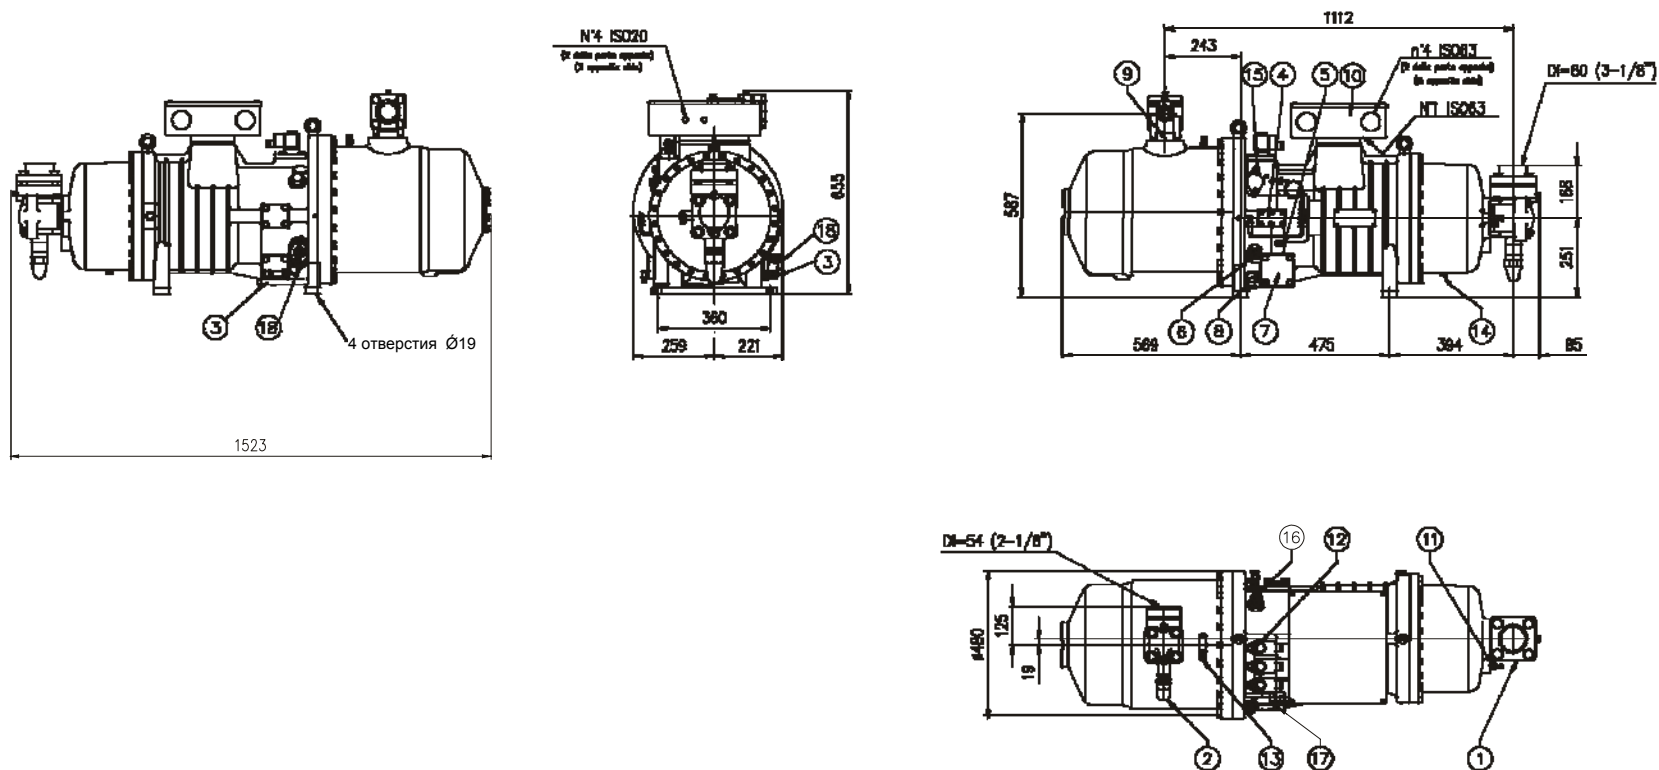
А: габаритный чертеж моделей: SRC-S-113/133/163 (код чертежа: MSI007 r.05);
